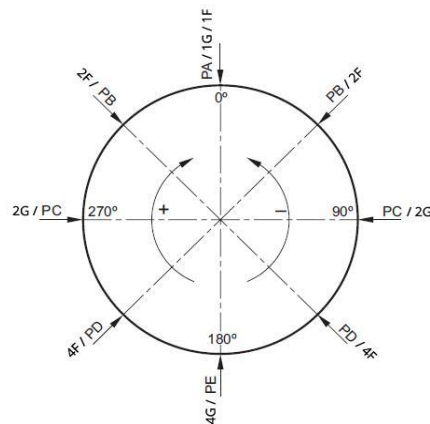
Posições de soldadura ISO 6947 [14]
